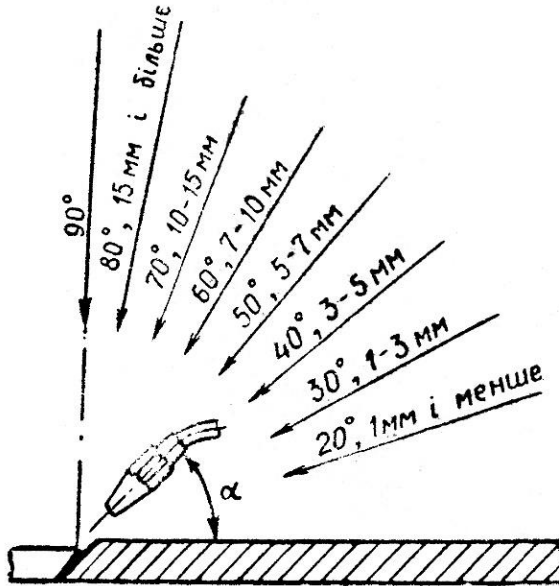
Залежність кута нахилу мундштука зварювального пальника від товщини зварювального металу
